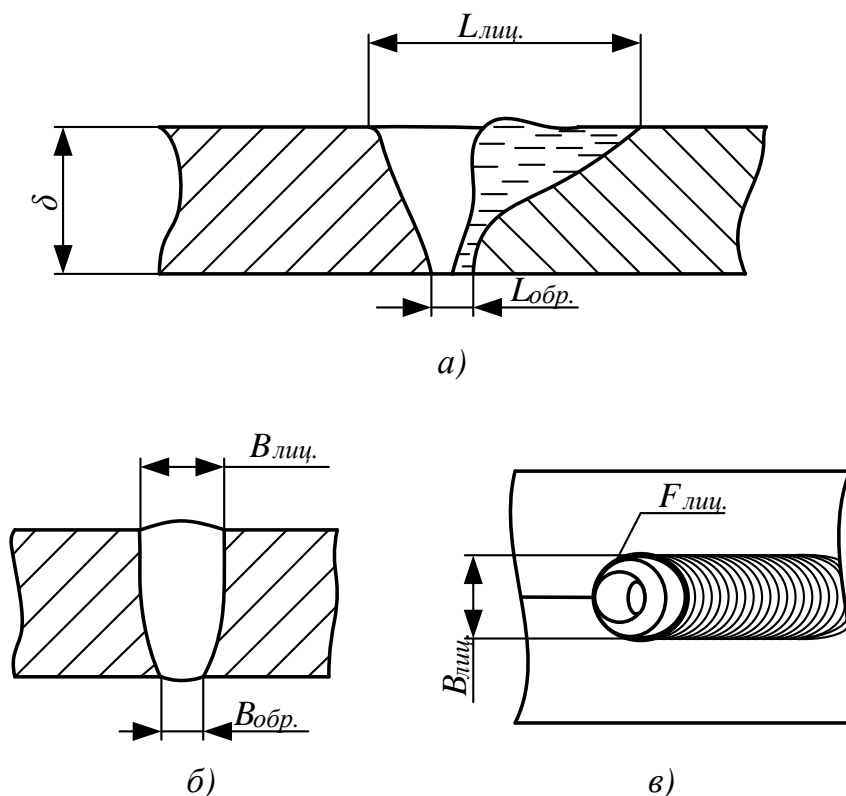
Схема сварочной ванны при сварке со сквозным проплавлением: а и б – продольное и поперечное сечения; в – вид сверху.
